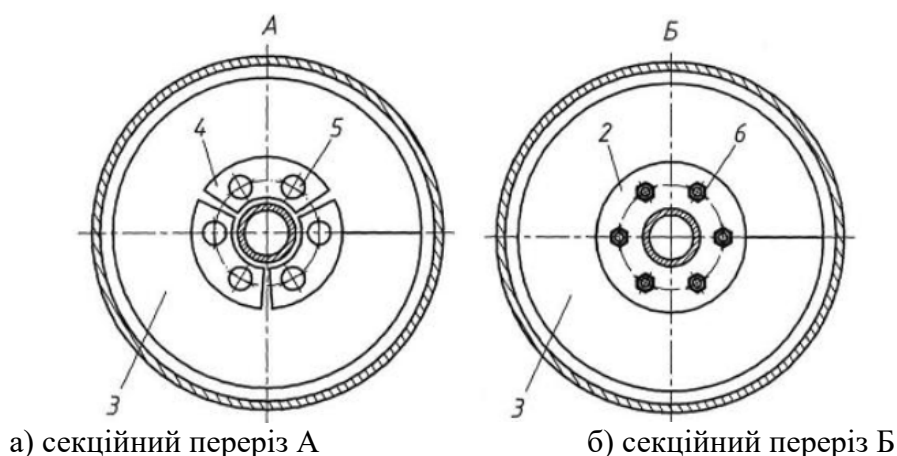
Поперечні перерізи А і Б модернізованого шнека з суцільною еластичною гвинтовою поверхнею: 2 – несуча смугова гвинтова спіраль; 3 – робоча еластична спіраль; 4 – секційна гвинтова пластина; 5 – болтове з'єднання з напівкруглою головкою; 6 – гайка з гравером
